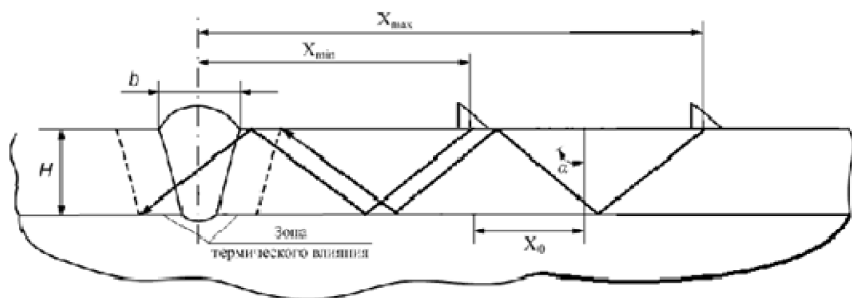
Схемы контроля сварных соединений многократно отраженным лучом
